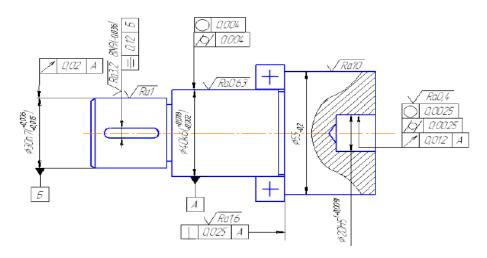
Шероховатость поверхностей и допуски на отклонение формы и взаимного расположения поверхностей вала и стакана подшипника.
